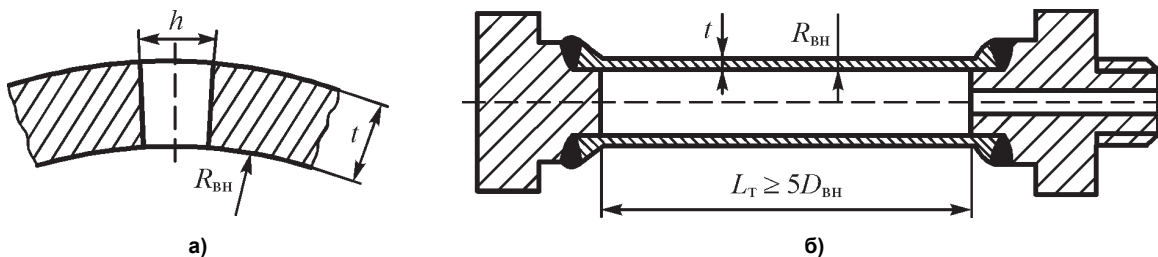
Сварное соединение с разупрочненным участком из сплавов типа АМг6Н и АМг6НПП, выполненное электронно-лучевой сваркой (а), и сварной цилиндрический образец для испытания на двухосное испытание (б)
